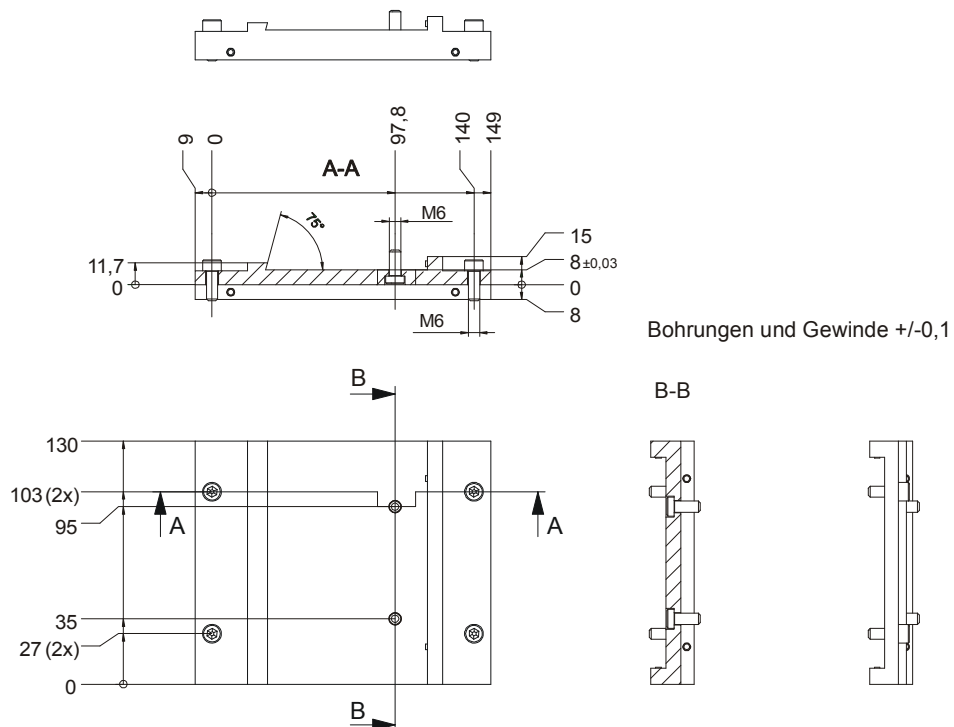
Adapterplatte 1067532, Maßzeichnung
